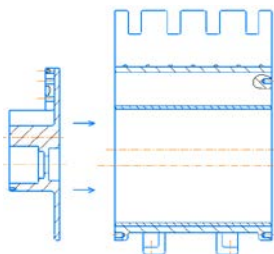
Схема присоединения крышки под ведомые валы к корпусу комбинированного насоса
